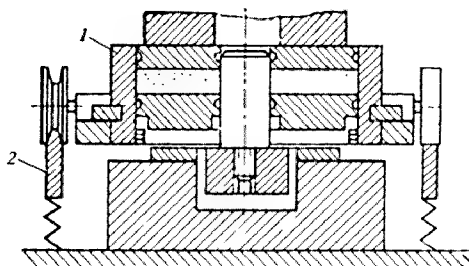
Схема прессования с подпрессовкой при подпружиненном рельсовом пути:
